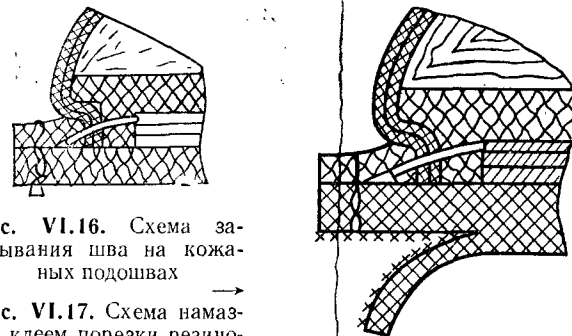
Схема закрывания шва на кожаных подошвах
